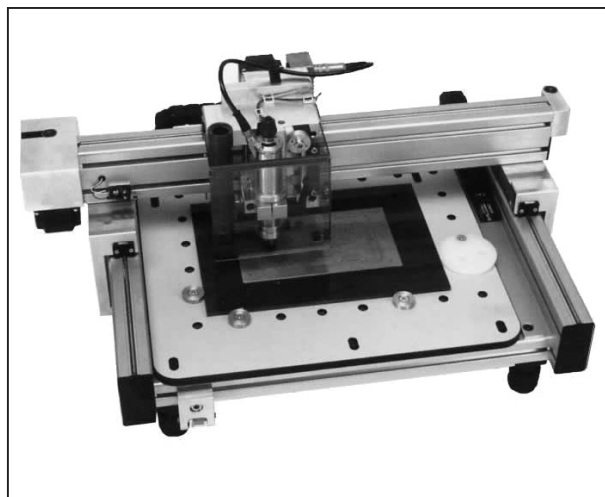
/8.3.19-9: De TechnoRoute machine van TechnoPrint-SMT.
